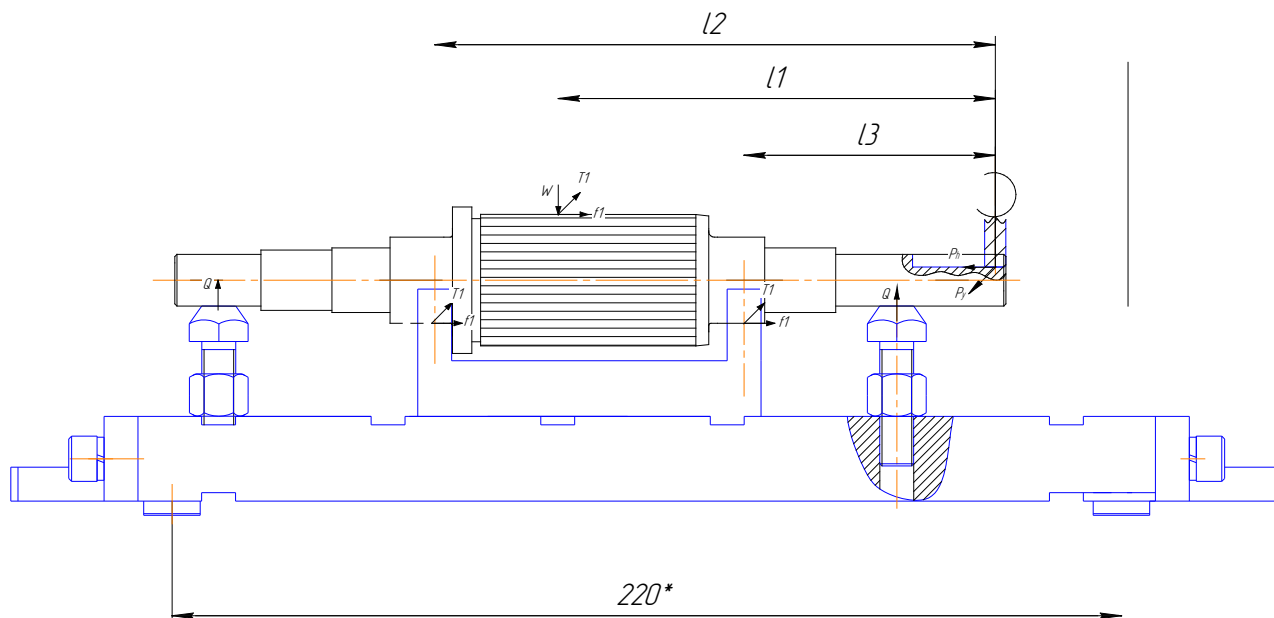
схема силового взаимодействия фрезы, заготовки и приспособления при обработке шпоночного паза.
